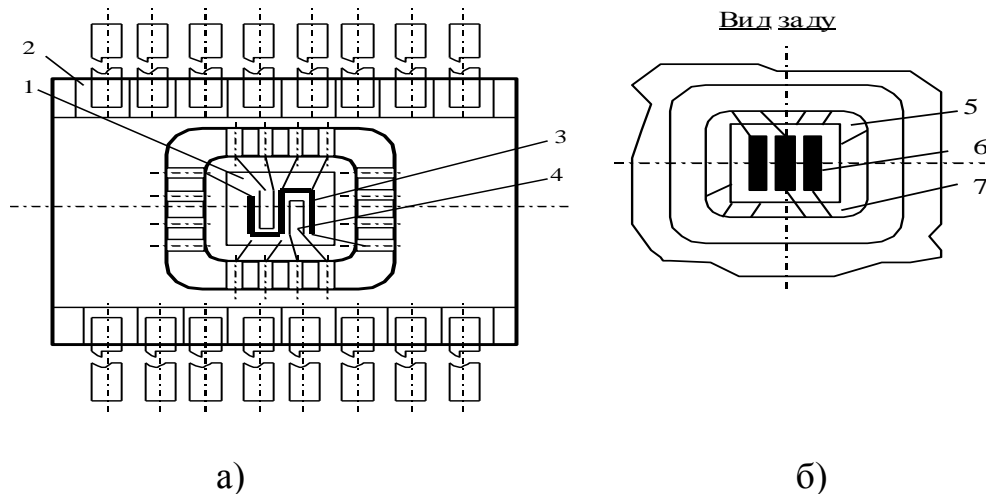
Типова конструкція напівпровідникового плівкового сенсора: 1 – модуль; 2 - корпус; 3 - нагрівач; 4 - терморезистор; 5 - чутливий елемент; 6 - електроди; 7 – виводи
